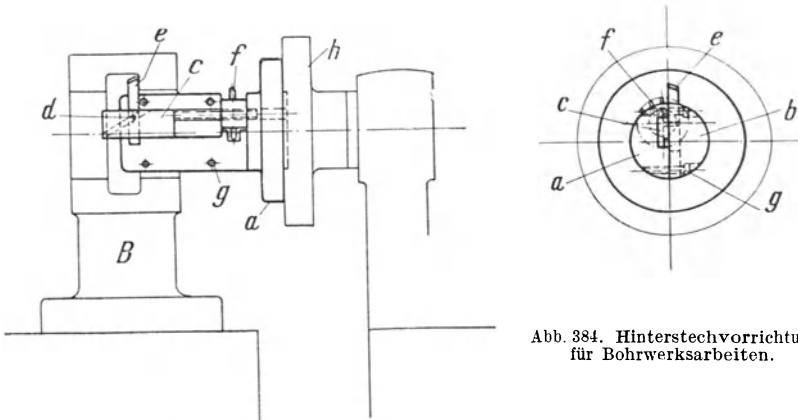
Hinterstechvorrichtung für Bohrwerksarbeiten.
